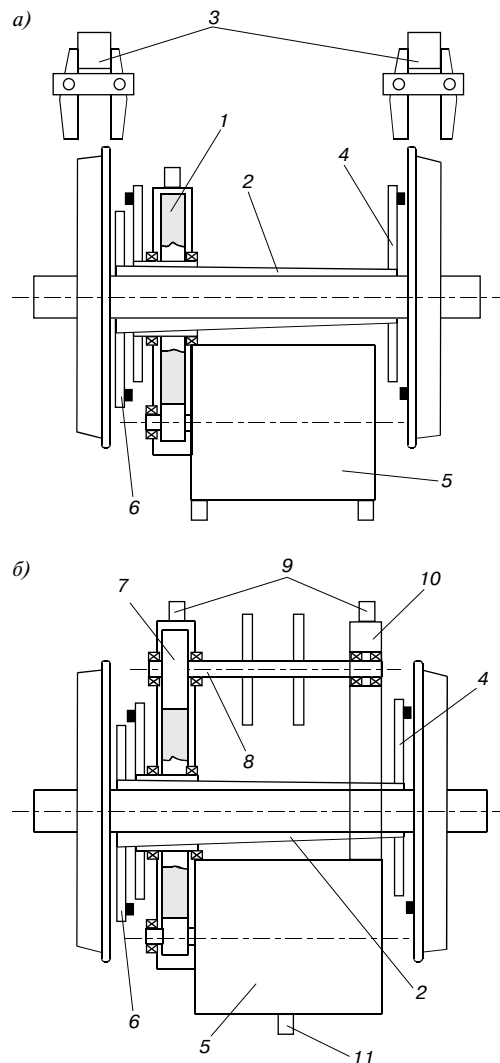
Полностью поддрессоренный тяговый привод с полным карданным валом:
